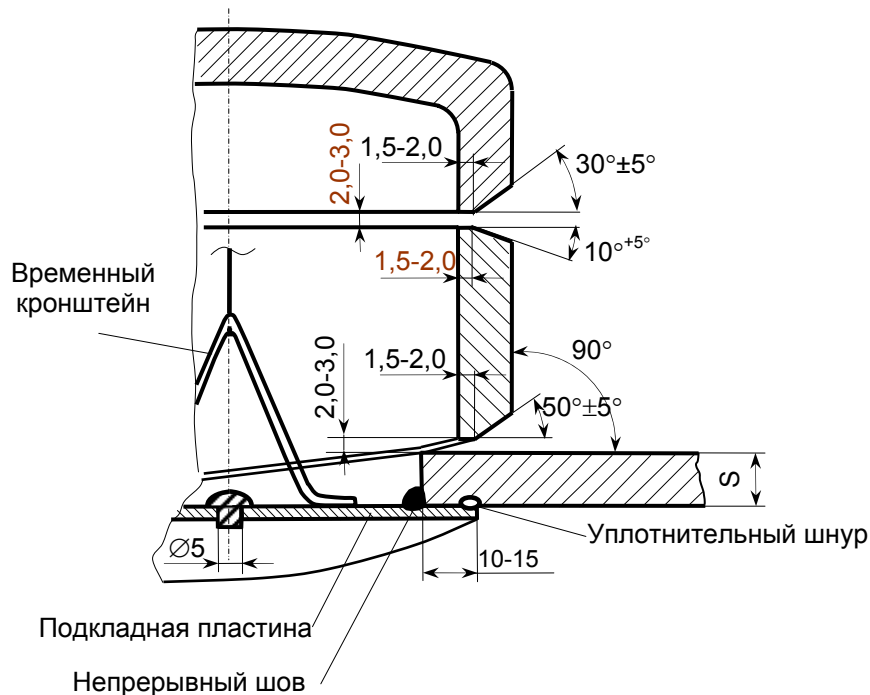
Параметры подготовки кромок патрубка и днища (заглушки)
